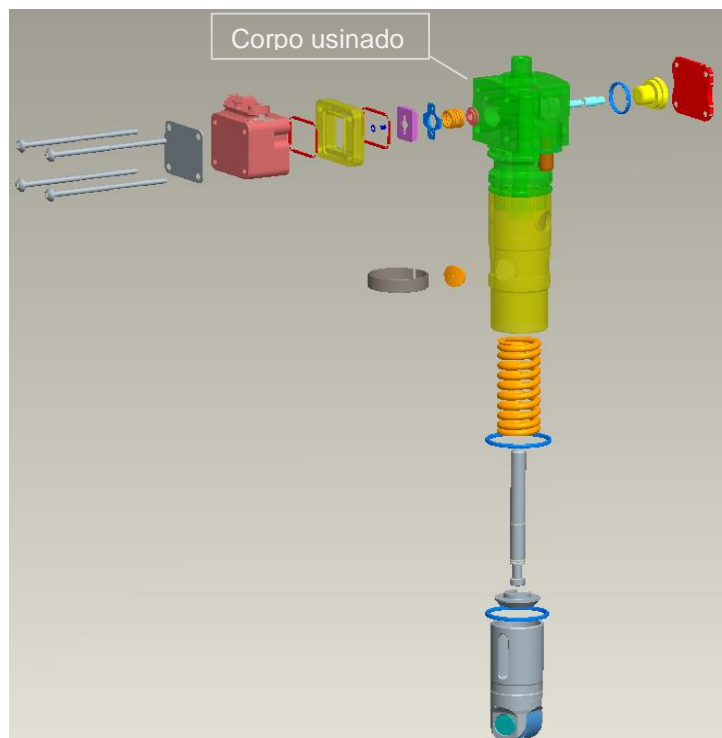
Representação do desenho em vista explodida da Unit Pump com seus componentes
